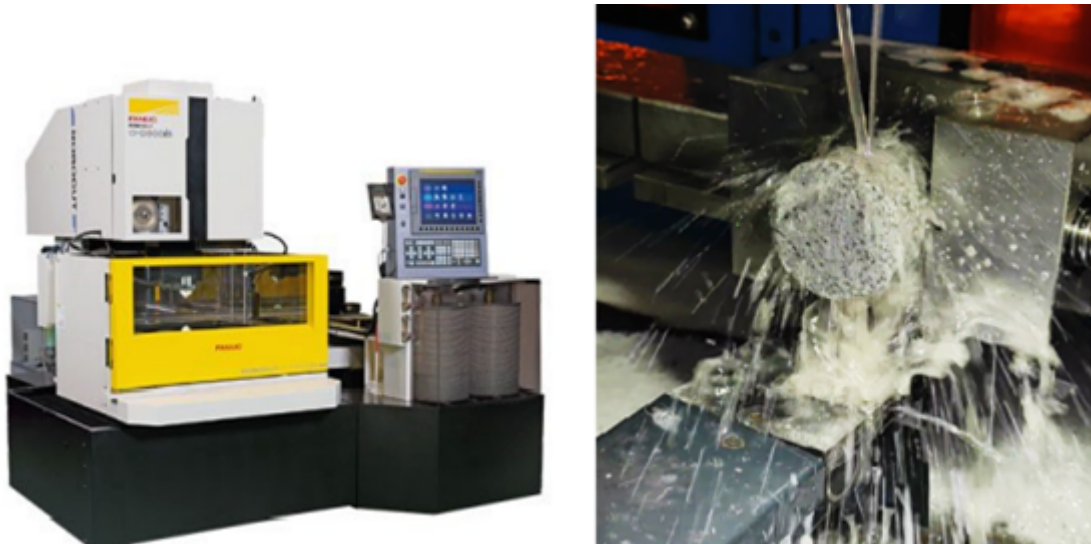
Le découpage des éprouvettes par fil électrique
